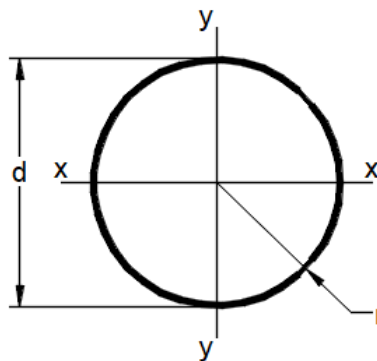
Forma de la soldadura en la base inferior del cabezal principal.
